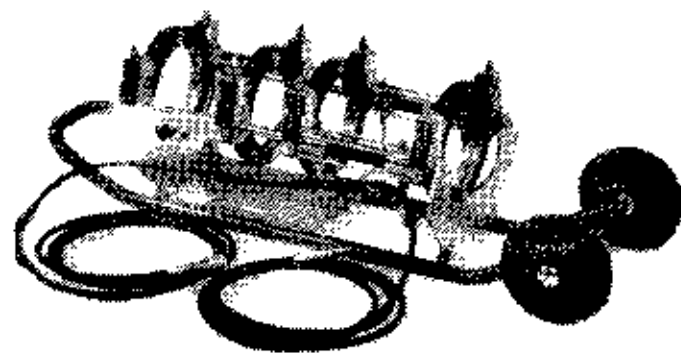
Центратор сварочной машины «Roweld- 250 Varioline» фирмы «Rothenberger» с поворотными зажимами
